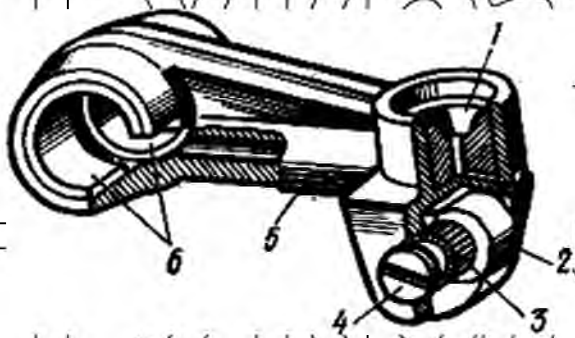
Пристрій роликового штовхача двигуна ЯМЗ-236. 1 – п'ята; 2 – ролик; 3 – голчастий підшипник; 4 – вісь; 5 – корпус штовхача; 6 – латунна втулка
